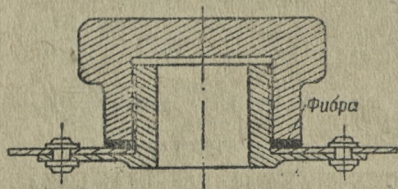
Приспособление для фиксирования фланца на баке перед клёпкой
